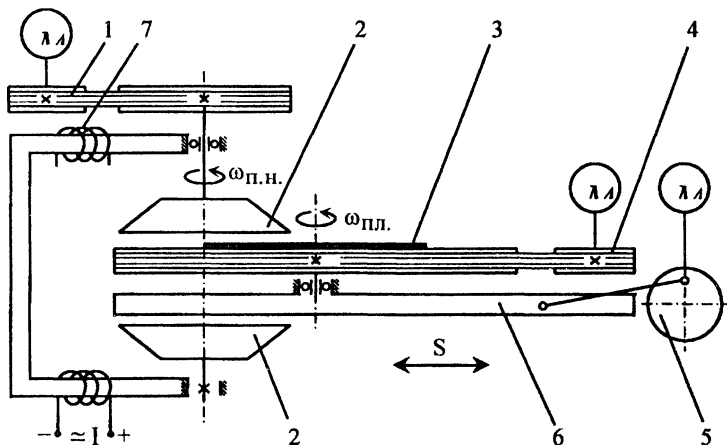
Схема магнитно-абразивной обработки кремниевых пластин: 1 – привод вращения полюсных наконечников; 2 – полюсные наконечники; 3 – обрабатываемая пластина; 4 – привод вращения пластины; 5 – привод подачи; 6 – каретка; 7 – электромагнитные катушки
